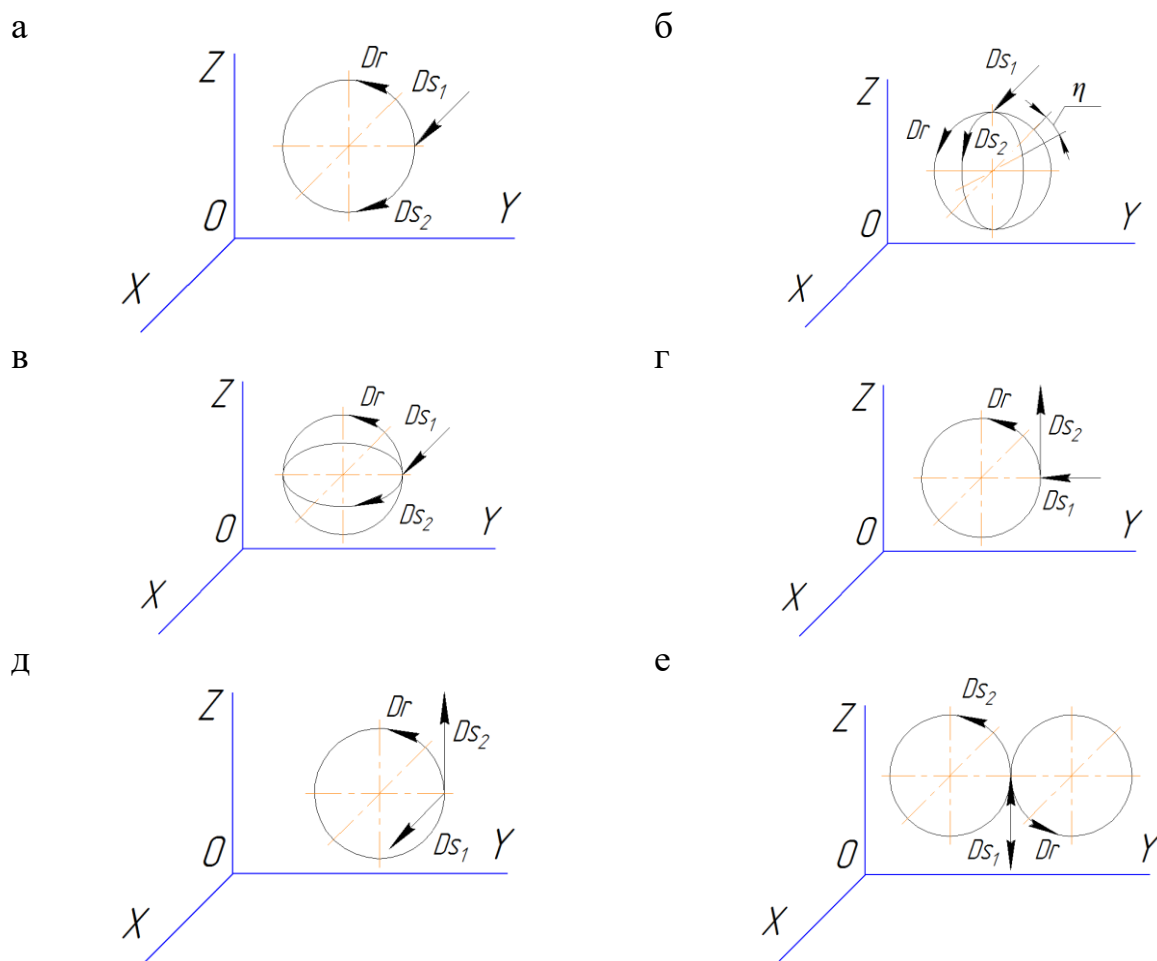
Кинематические схемы резания: *a* – обработка охватывающими фрезами (зенкерами) цилиндрической или конической поверхности; *б*, *в* – обработка охватывающими фрезами (зенкерами) неполной сферической поверхности; *г* – обработка с врезанием фрезы по дуге уступа или полузакрытой полости; *д* – обработка с врезанием фрезы по касательной плоской поверхности детали; *е* – обработка с врезанием фрезы по касательной плоской и цилиндрической поверхностей детали
